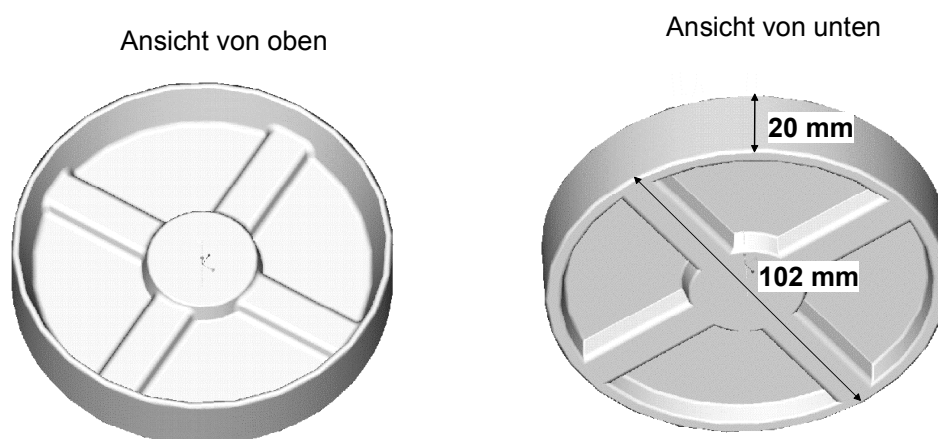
Obere und untere Ansicht des Magnesiumbauteils aus dem CAD-Programm ProEngineer
